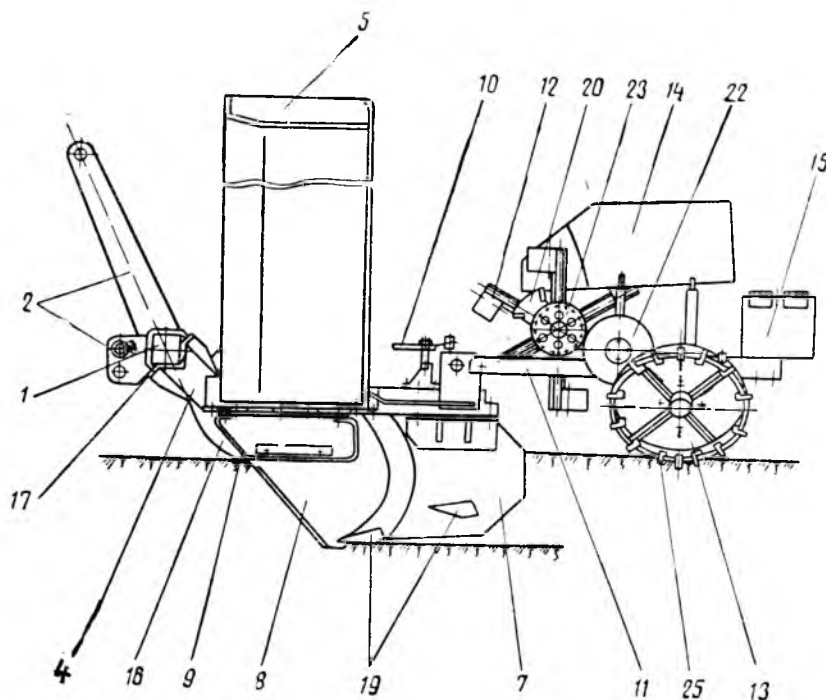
Схема лесопосадочной машины СЛТ-2 (вид сбоку)
